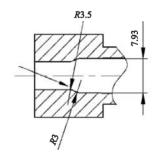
改进后铸件结构 Fig. 3 Improved structure of casting
